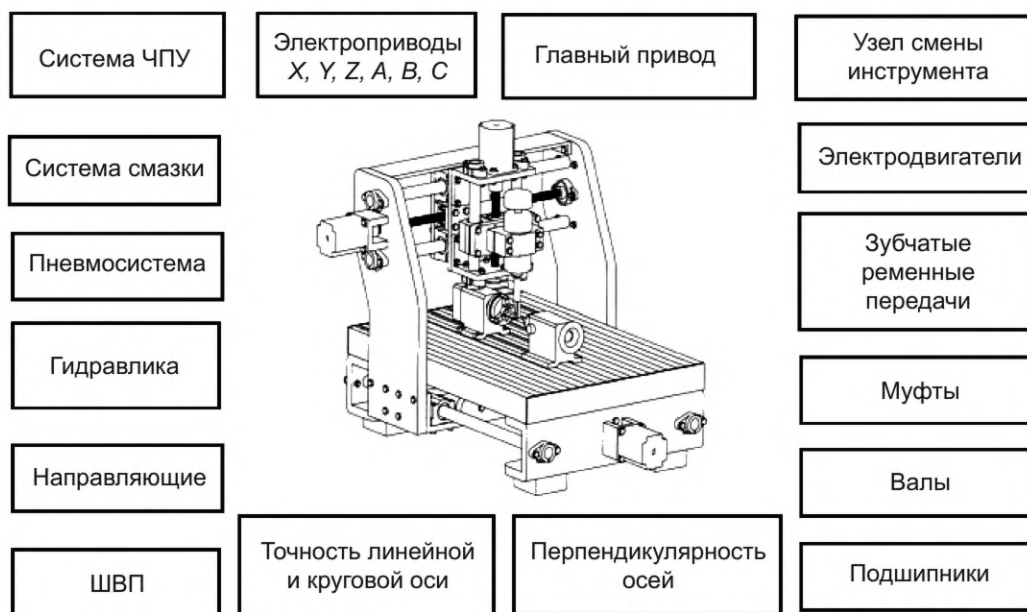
Типовая структура станка для токарно-фрезерной обработки
